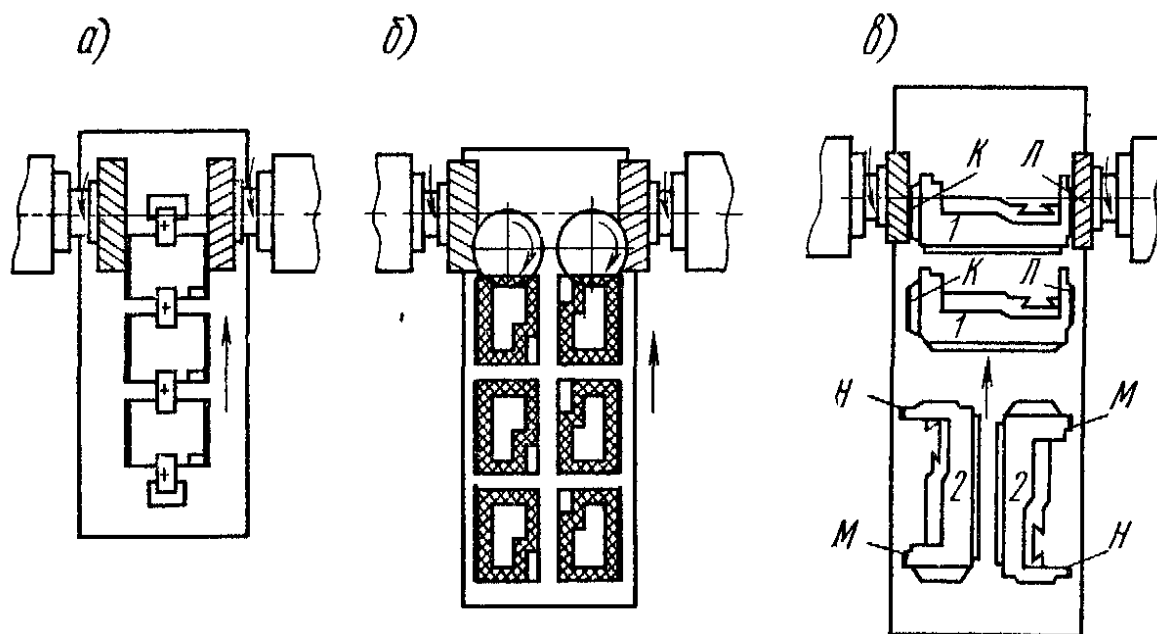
Групповая обработка корпусных деталей на продольно-фрезерном станке
